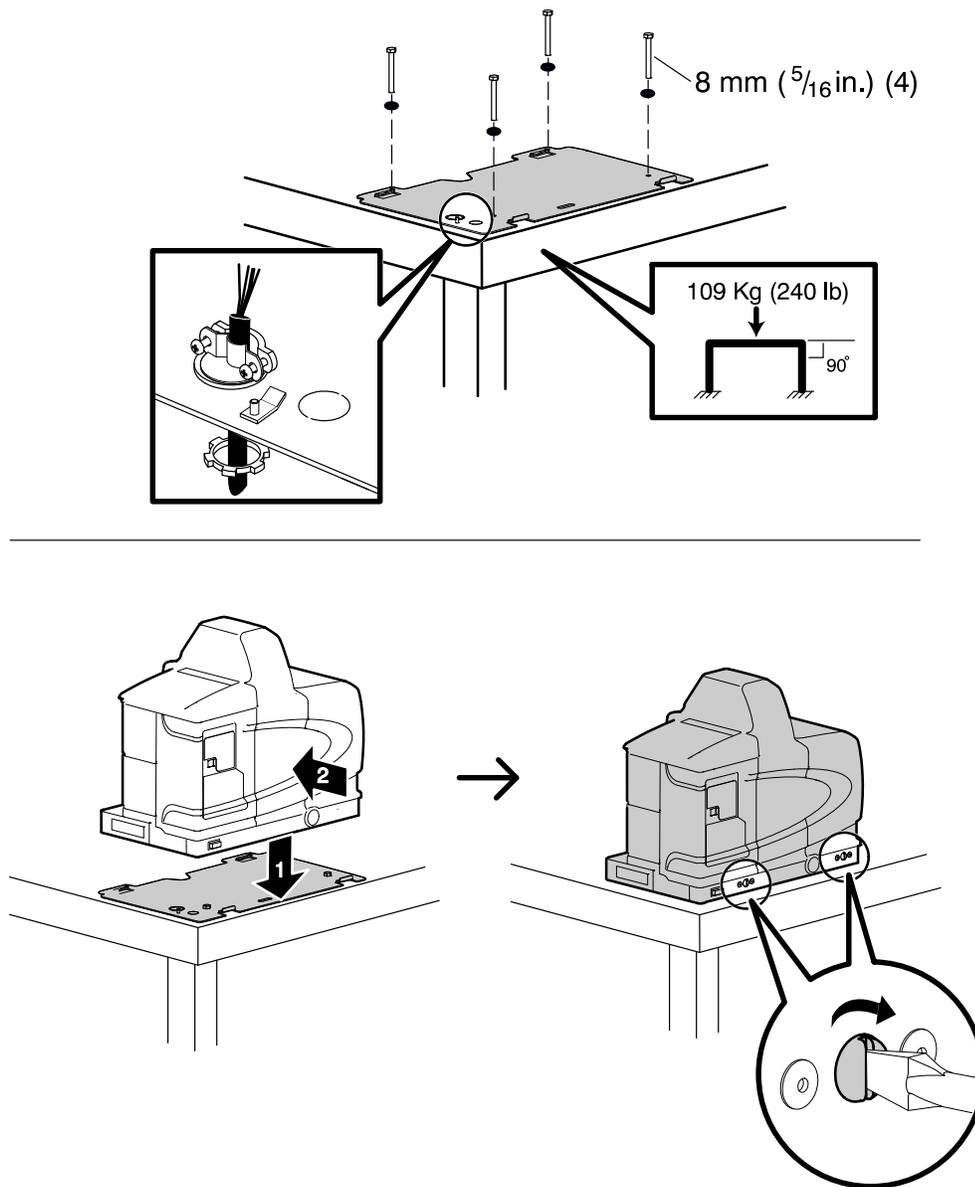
Montaggio della sottobase e dell'unità di fusione
